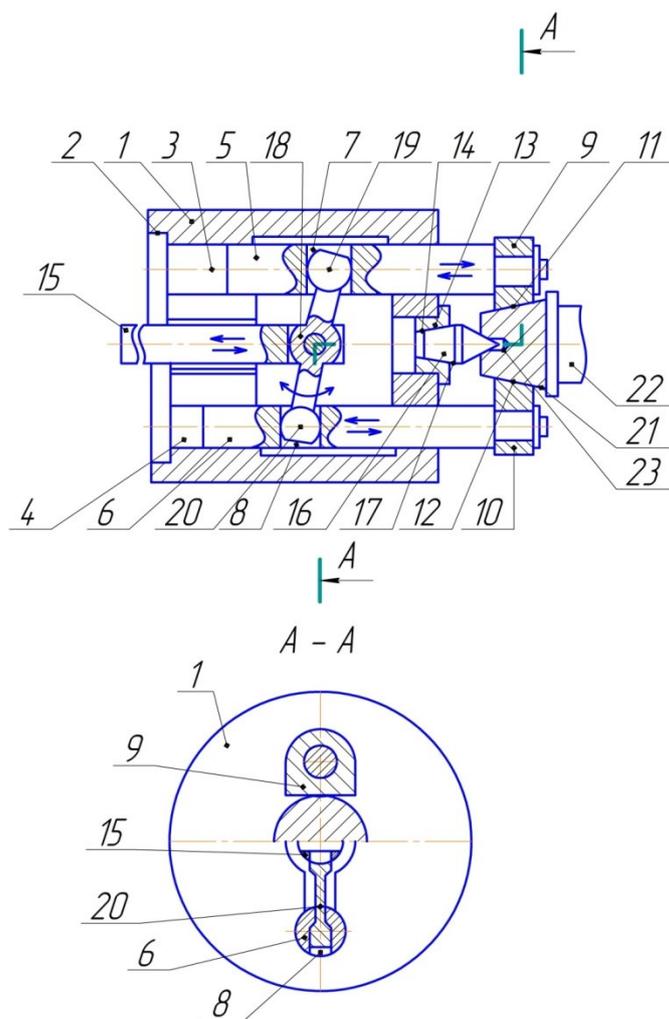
Схема патрона кулачкового механизированного для установки вала с конической поверхностью на центрах станка
